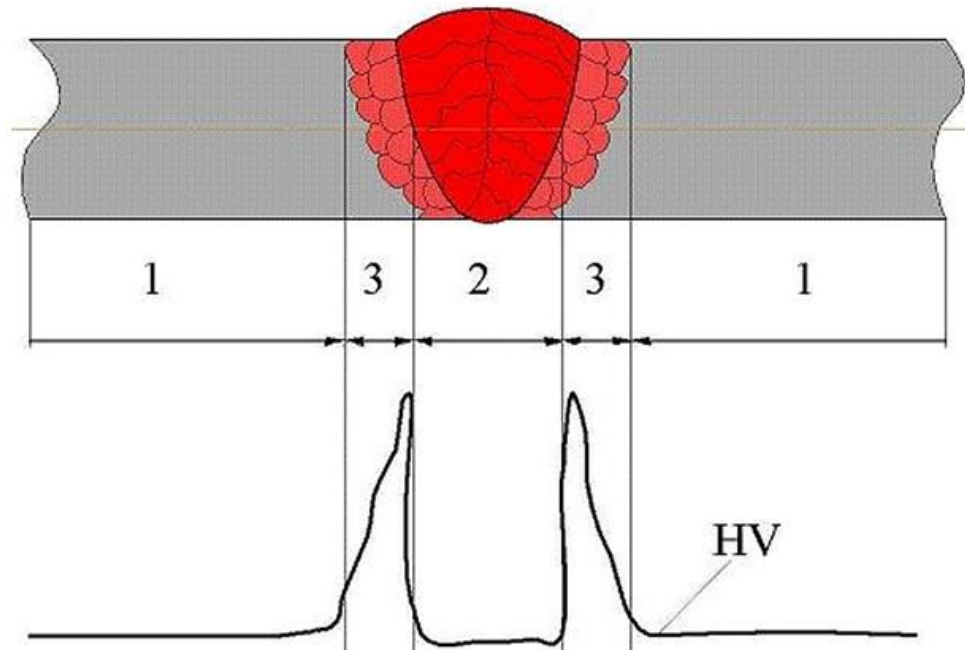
Орієнтовна схема розподілення твердості (HV) в різних зонах зварного з'єднання: 1 – основний метал, 2 – наплавлений метал, 3 – метал ЗТВ [118]
